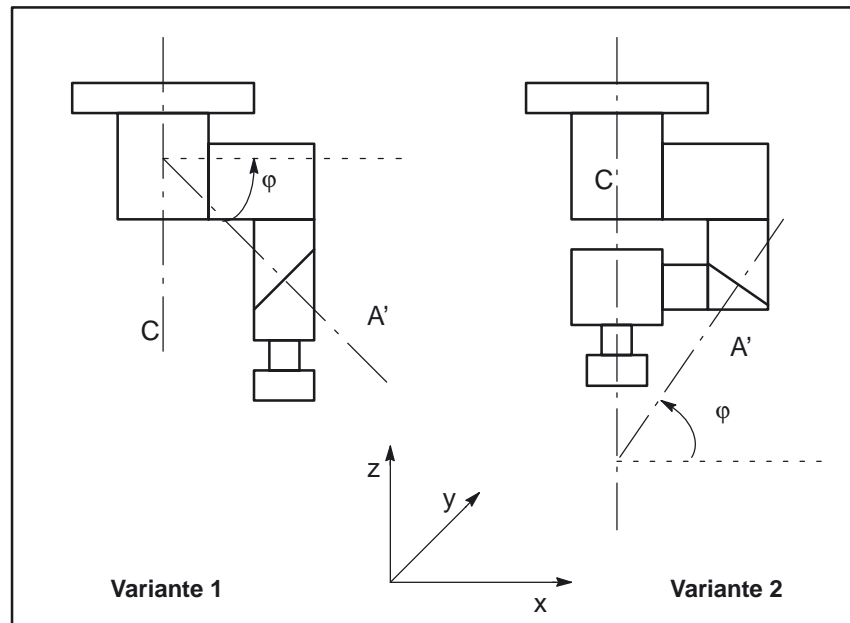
Kardanischer Werkzeugträger mit zwei Achsen
